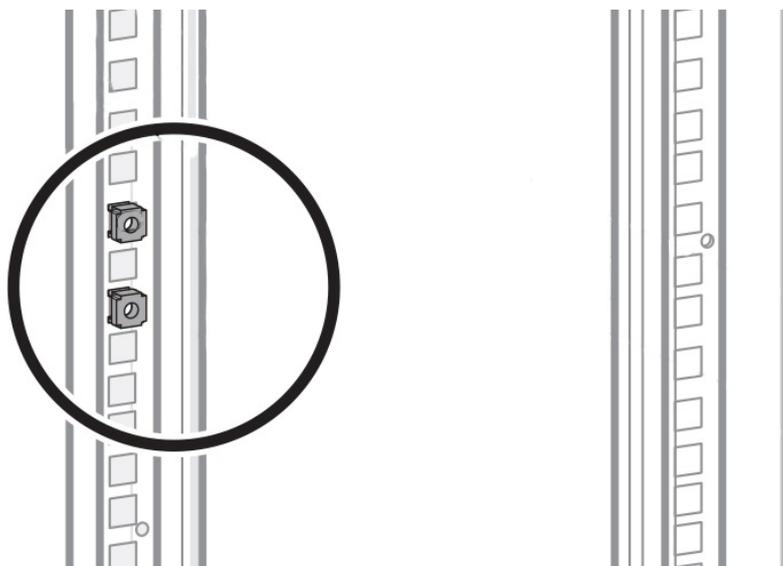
Установка клетевых стоечных гаек в монтажной стойке.
